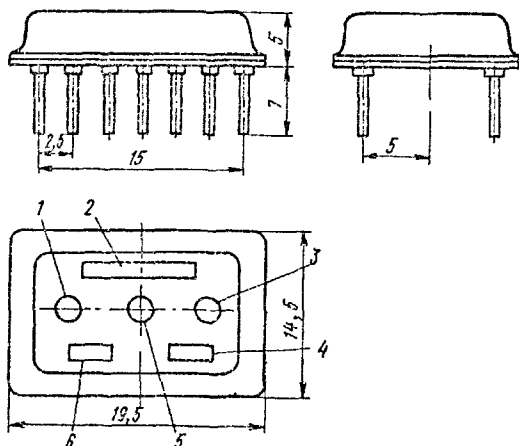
Габаритные и присоединительные размеры фильтров ФПЗП9-451
